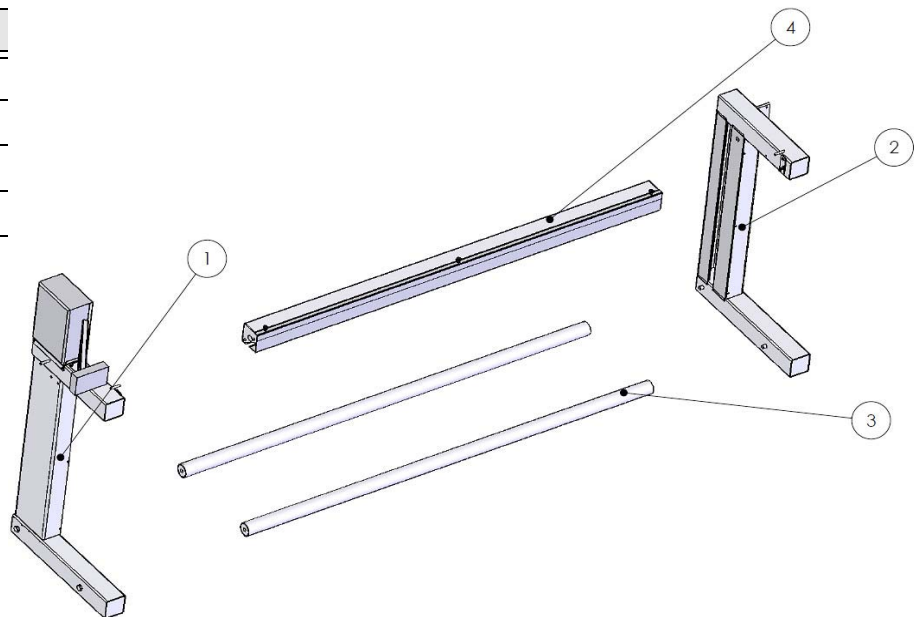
Ersatzteilzeichnung 2 (Baugruppe des Maschinenrahmens) LBSM ESE Modelle
